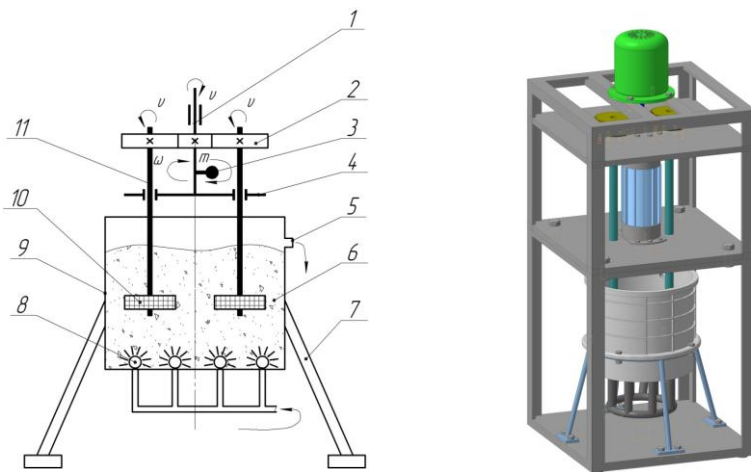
Принципиальная схема и общий вид лабораторно-промышленного вибростанка для реализации мультиэнергетических технологий: 1 – шпиндель; 2 – зубчатое зацепление; 3 – вибровозбудитель; 4 – приспособление; 5 – отвод; 6 – рабочая среда; 7 – жесткая опора; 8 – гидродинамические устройства; 9 – резервуар; 10 – обрабатываемая деталь; 11 – установочные пальцы.
